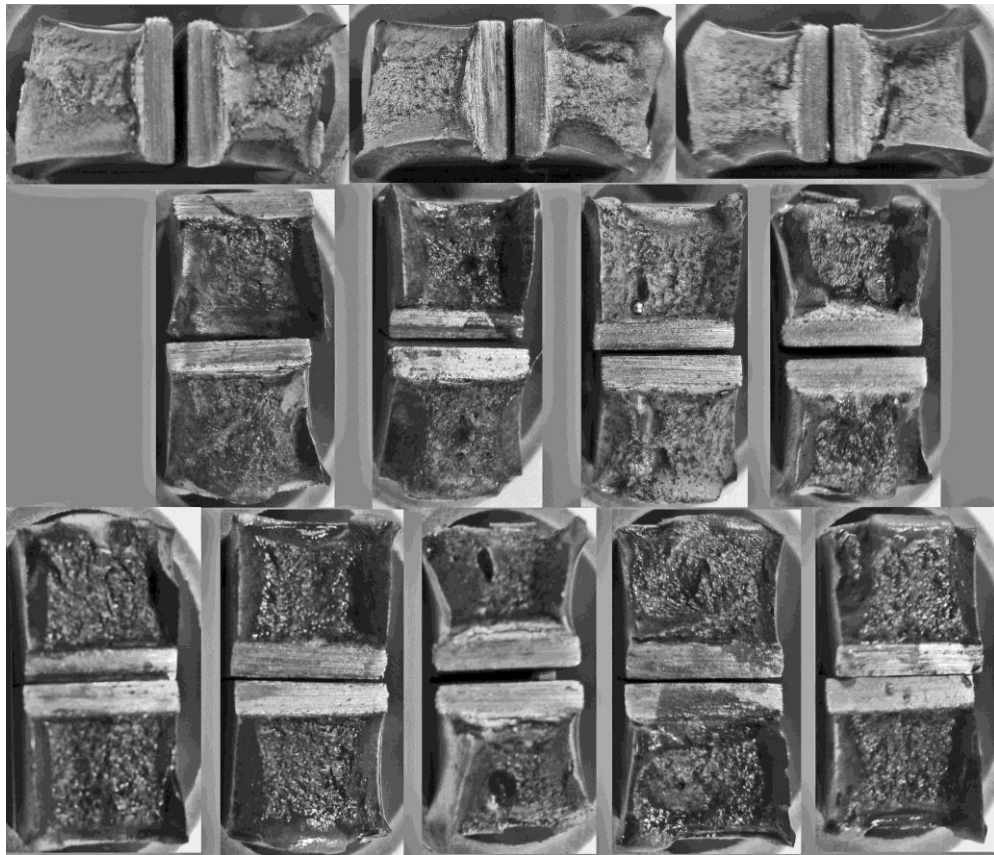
Fotografias das superfícies de fratura do ensaio Charpy-V, dos corpos de prova soldados com 40 °C de pré-aquecimento.
